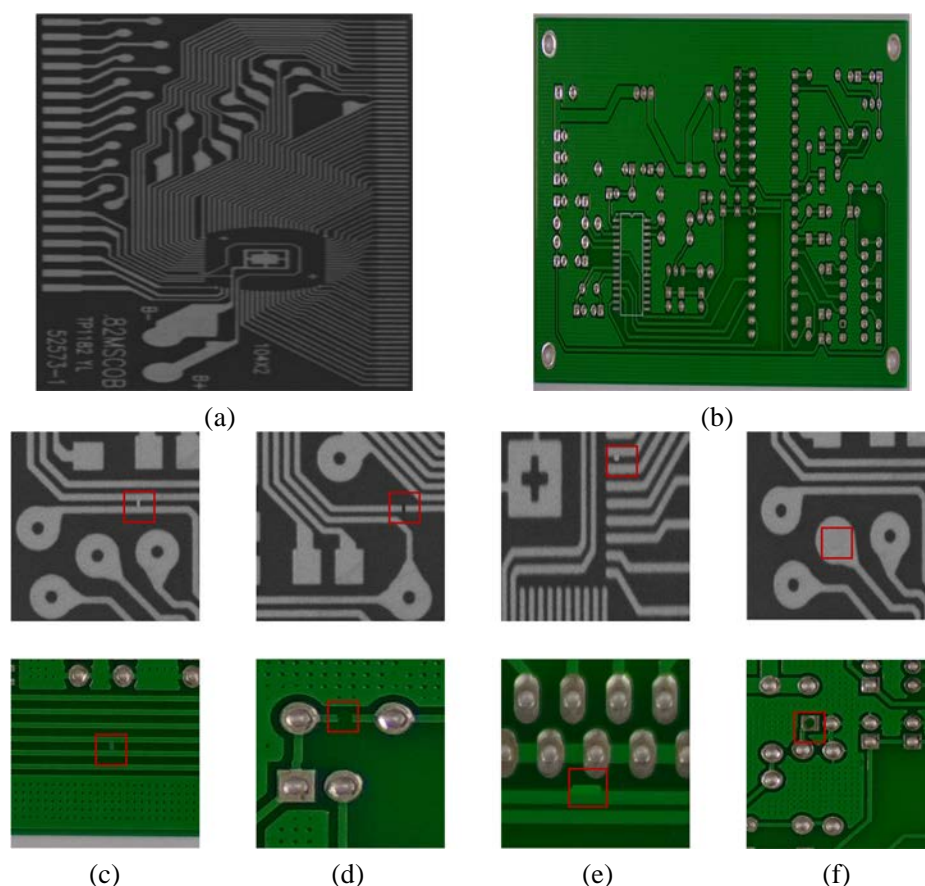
本文 PCB 图像：(a) PCB 裸板图像；(b) PCB 板图像；(c) 短路；(d) 开路；
